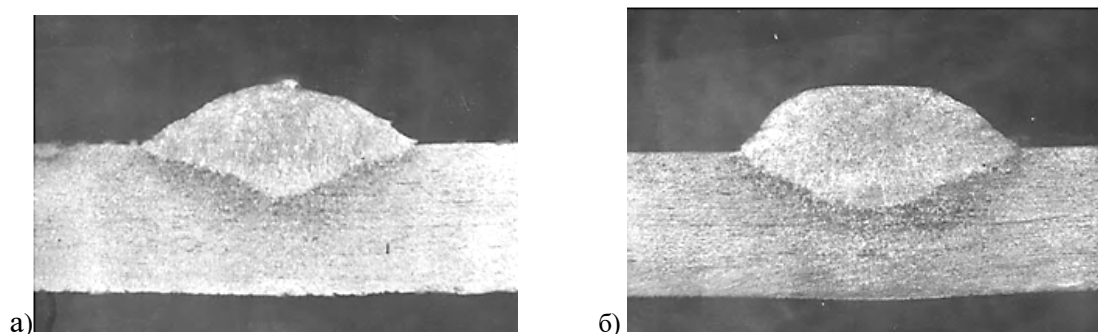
Макрошлиф сварного шва, по базовой (а) и предлагаемой технологии сварки (б)
